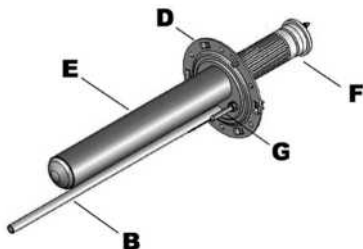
Стативный нагревательный элемент + анод PROfessional TECH
